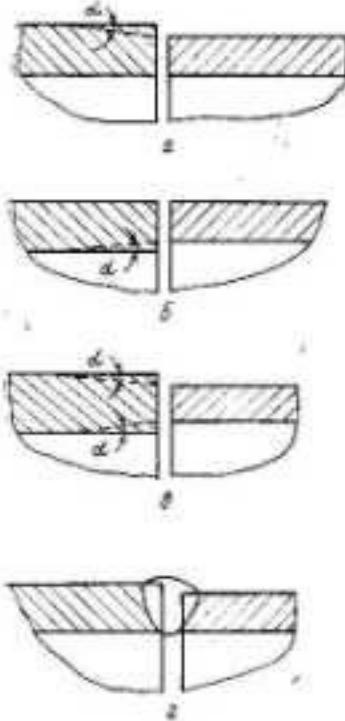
Схемы обработки концов труб и деталей различной толщины под сварку:
